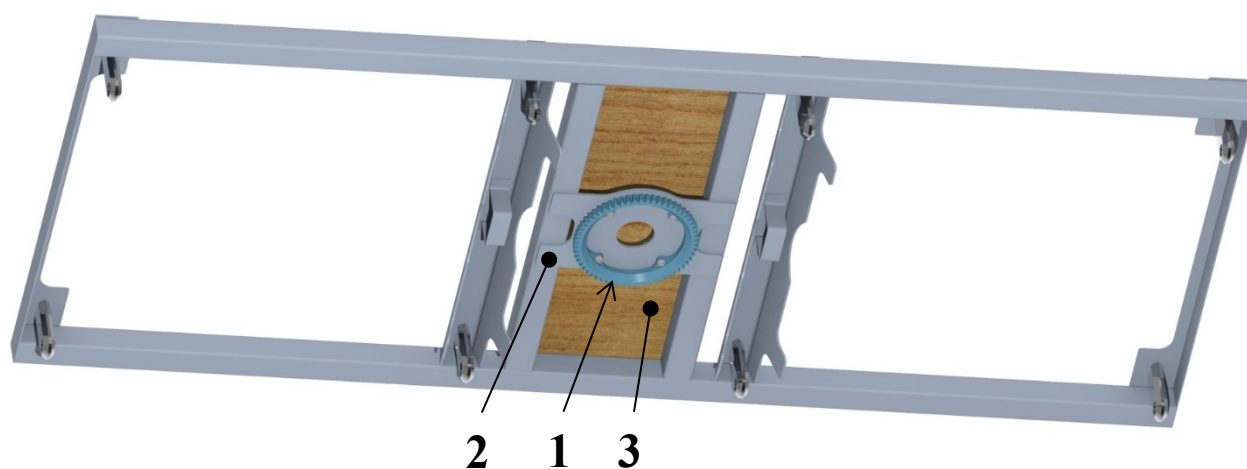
Detailní pohled na pozici číslo 1
